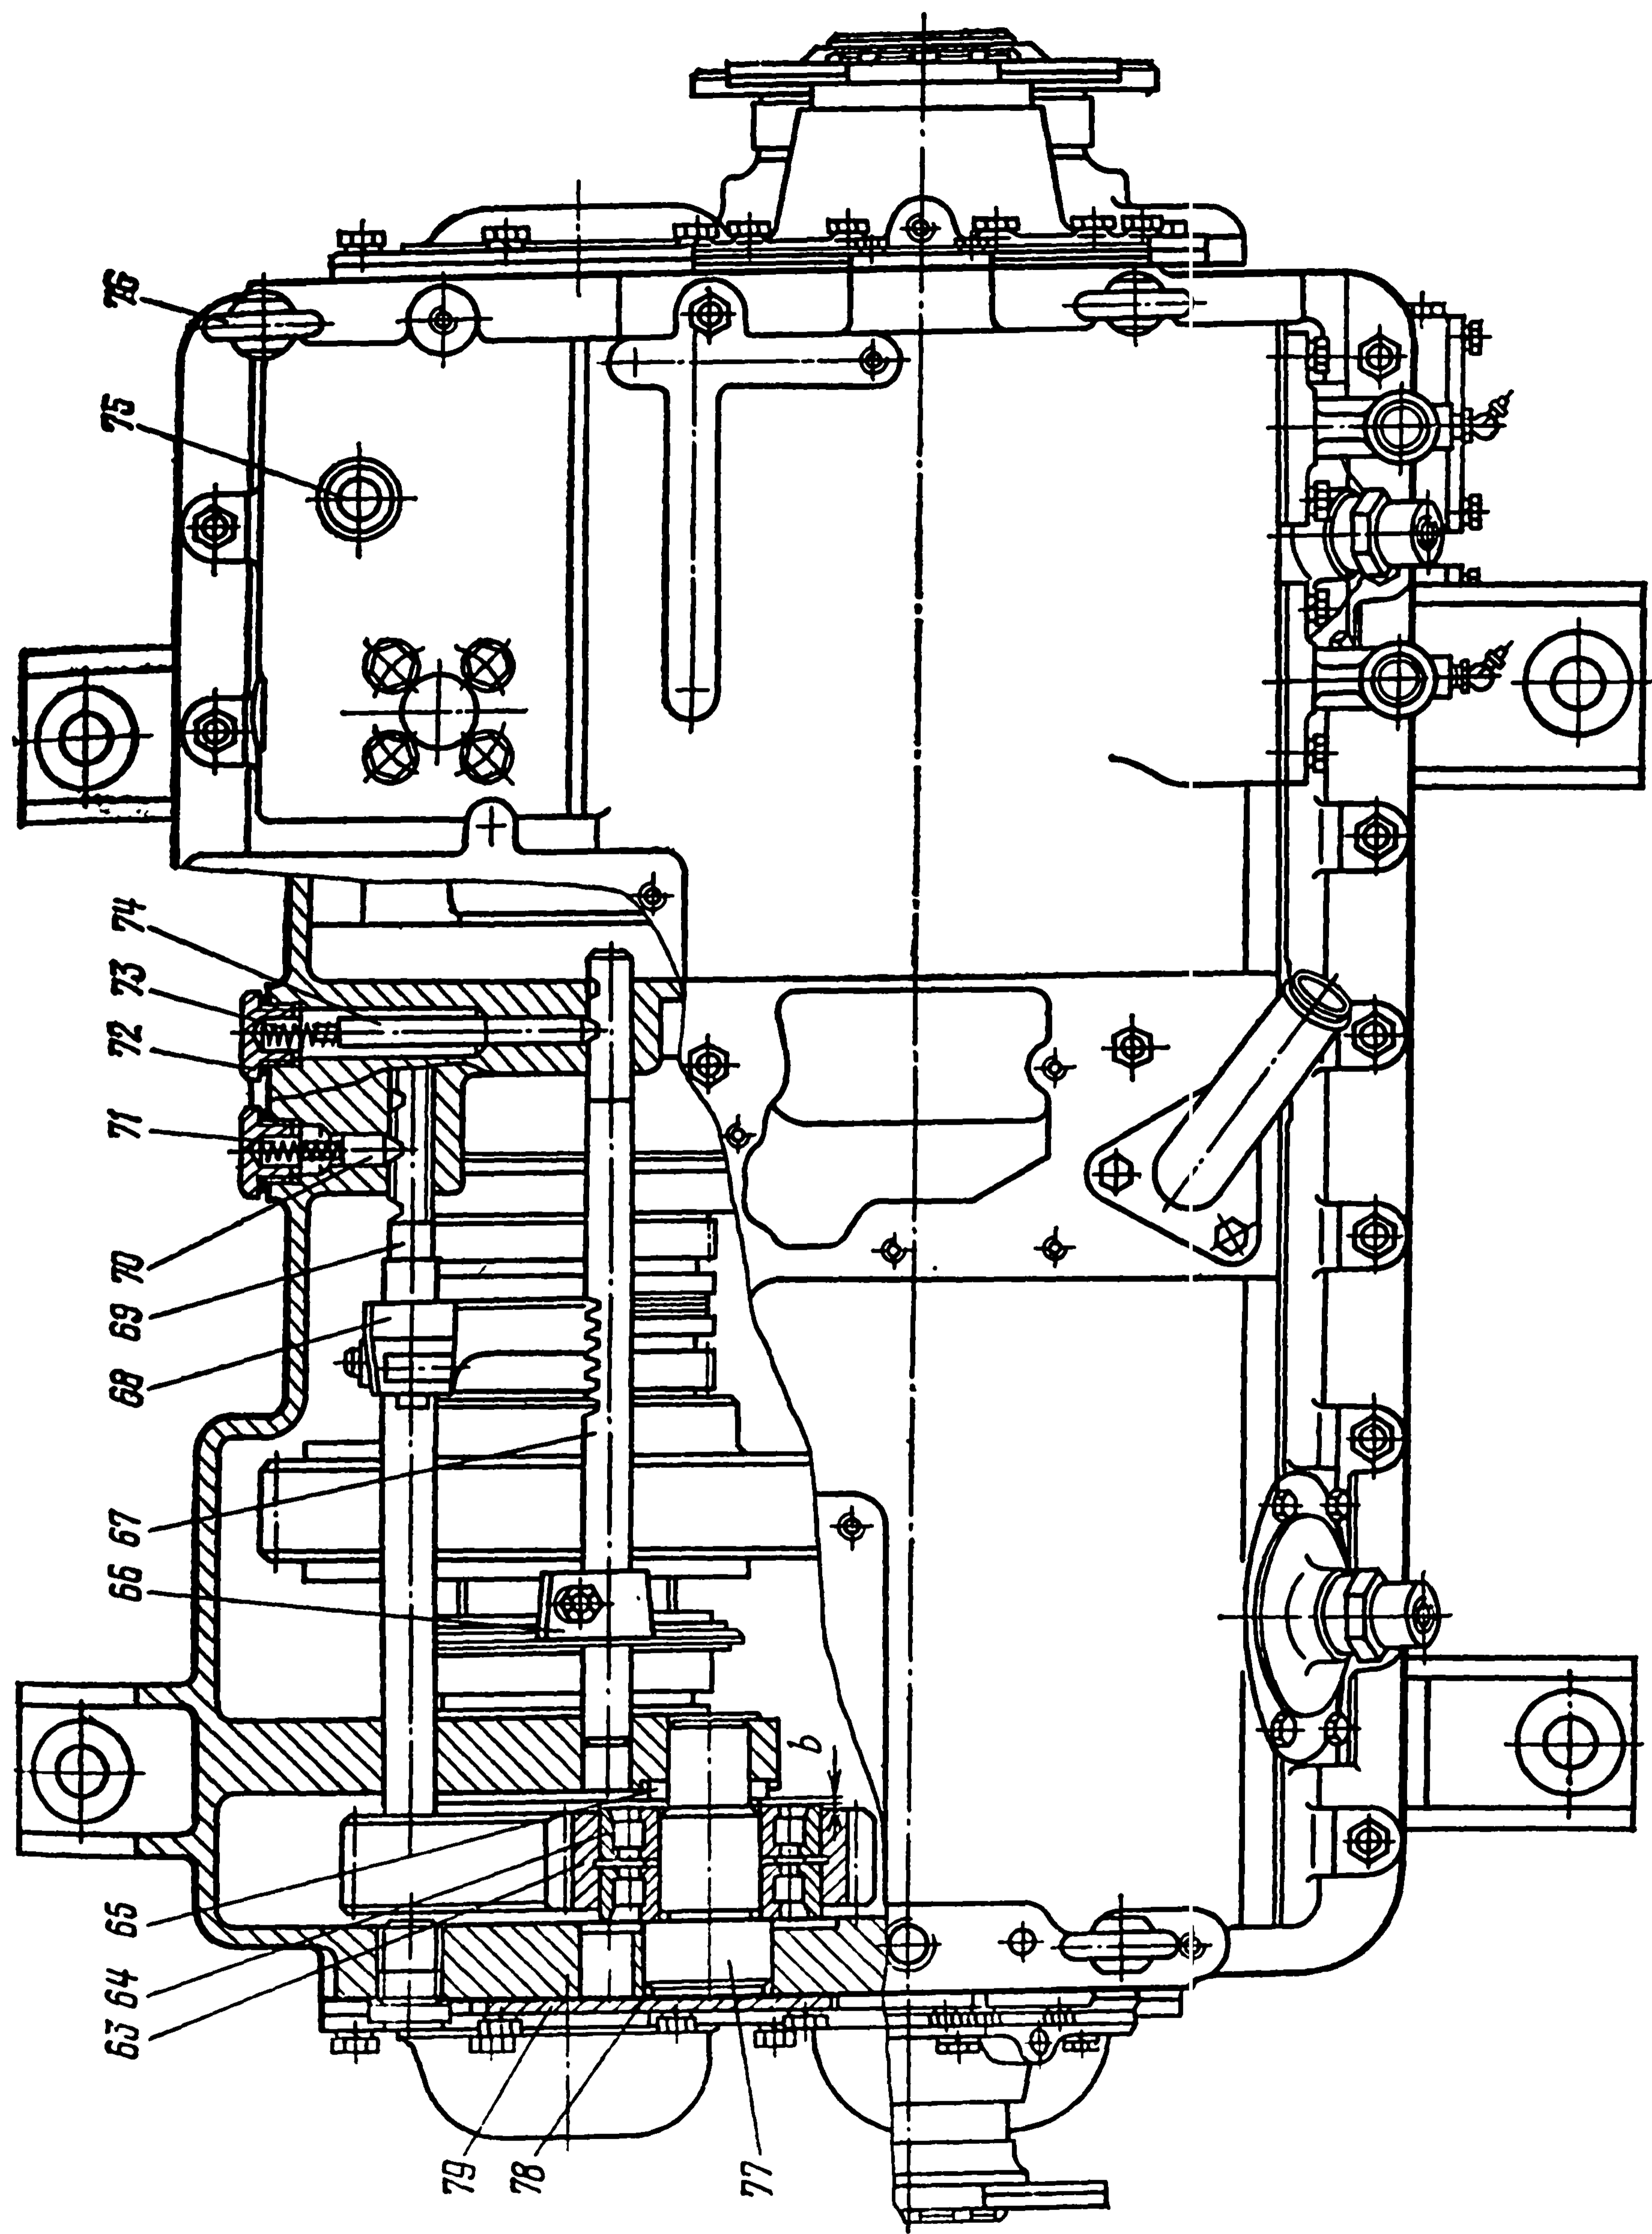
Редукторная часть (вид сверху) коробки передач (продолжение):
